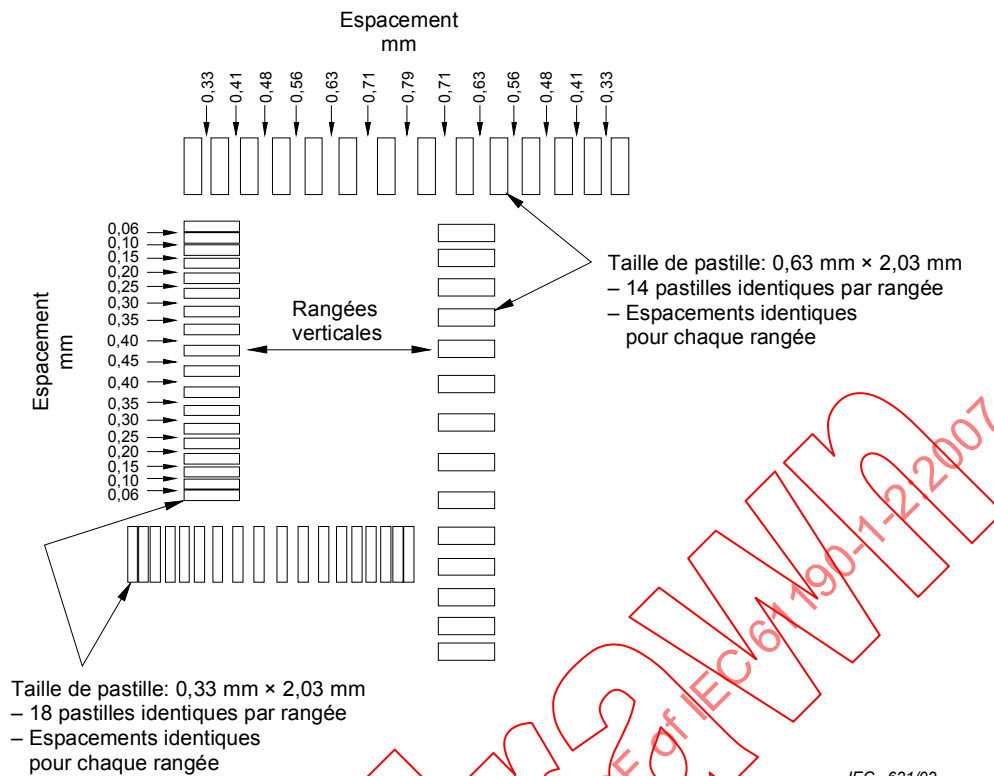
Epaisseur du pochoir de l'essai d'affaissement, 0,20 mm
